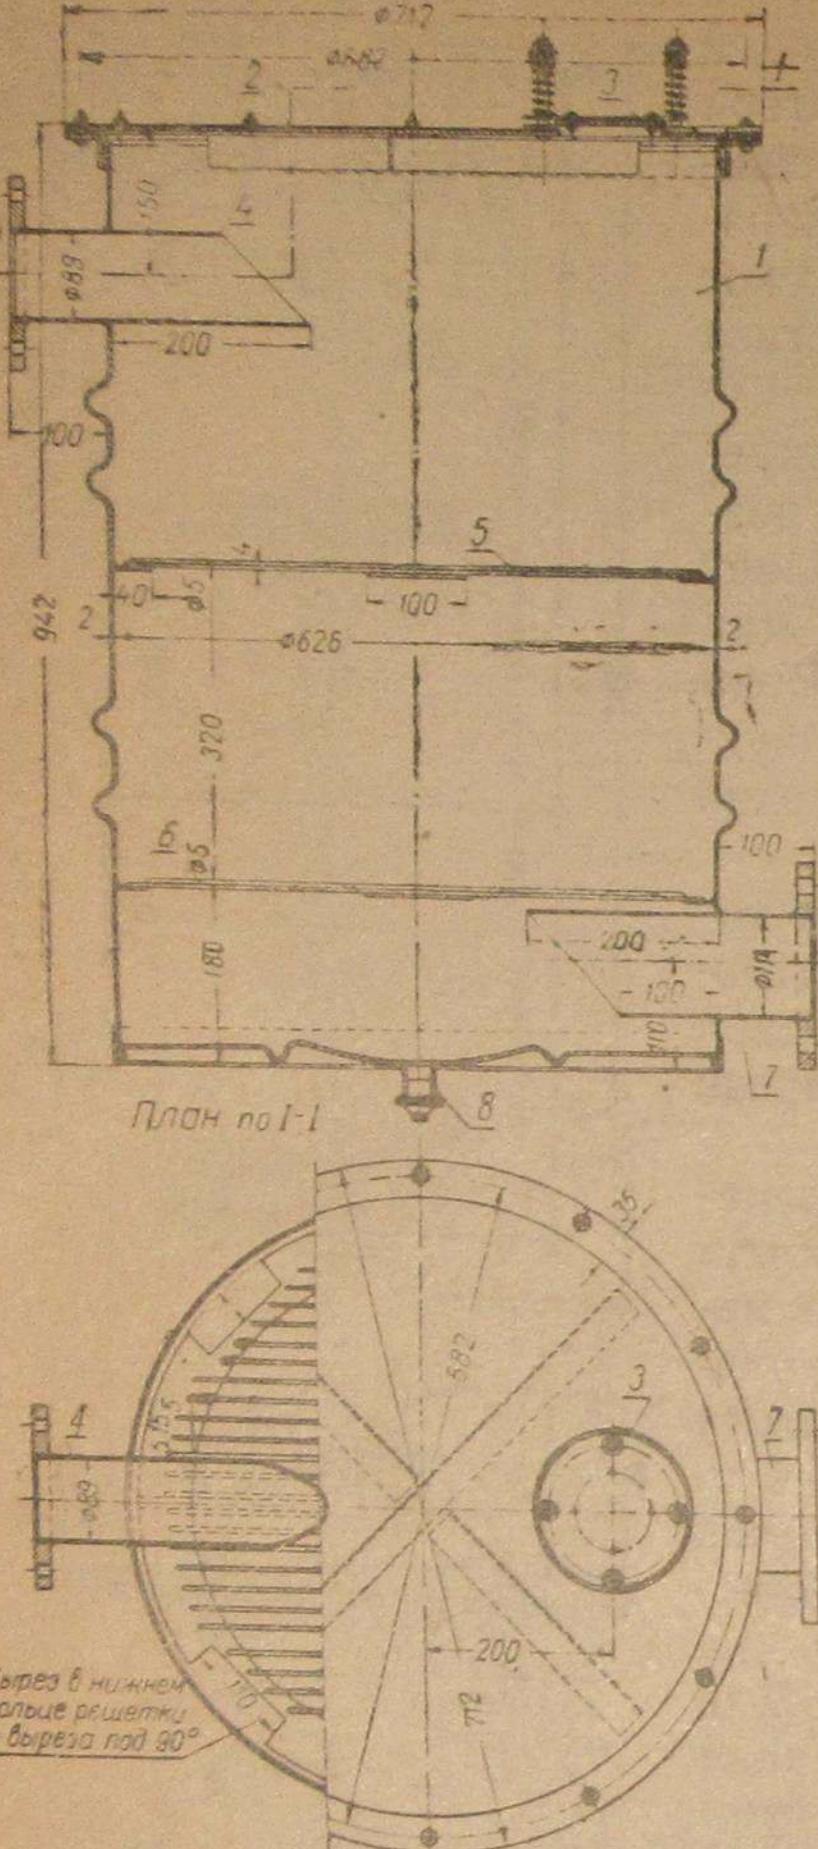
Скру́ббер производительностью 100 м<sup>3</sup> газа в час, изготовленный из листовой стали толщиной 3 мм (II вариант): 1—корпус скру́ббера; 2—крышка скру́ббера; 3—оросители; 4—газоотводный патрубок; 5—люк для разгрузки насадок; 6—деревянная решётка для укладки насадок; 7—газоподводящая труба; 8—чаша; 9—переливная труба; 10—пробка для спуска воды
